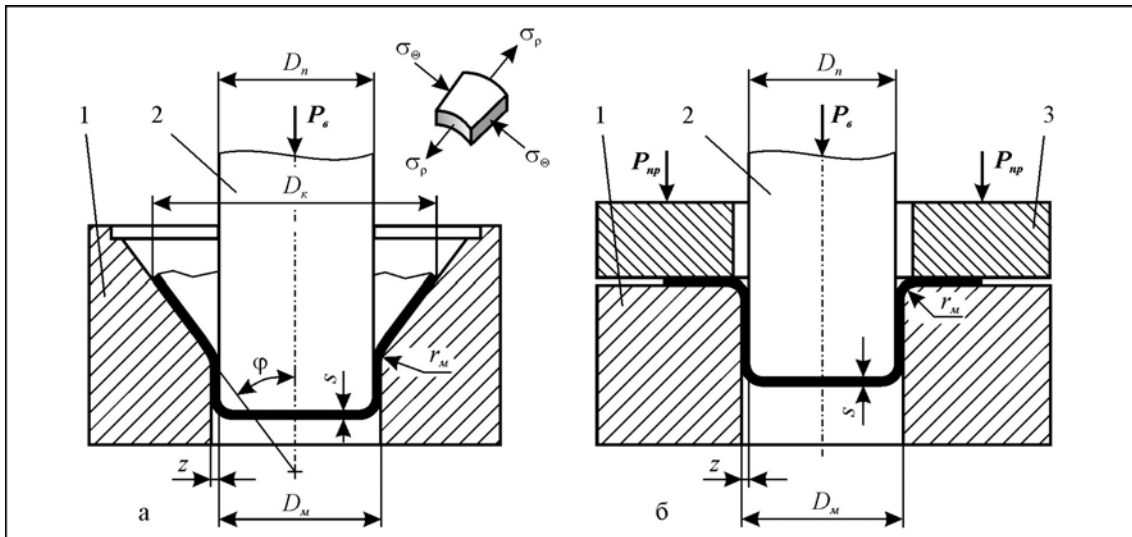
Схема штамів для першого витягування: а – без притиску фланця заготовки; б – з притиском фланця заготовки
